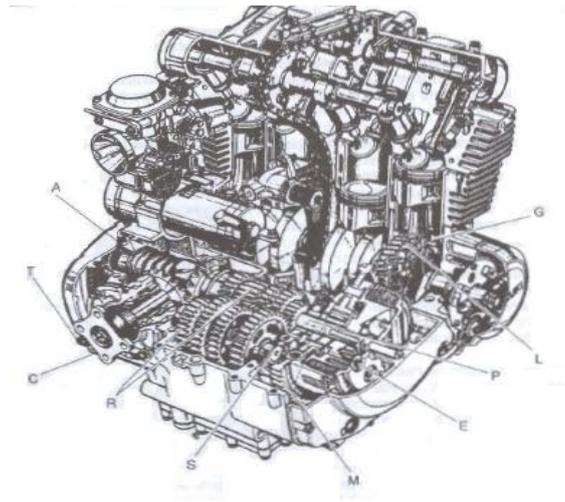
Elementos de la transmisión de una Suzuki GSX 750 c.c.
